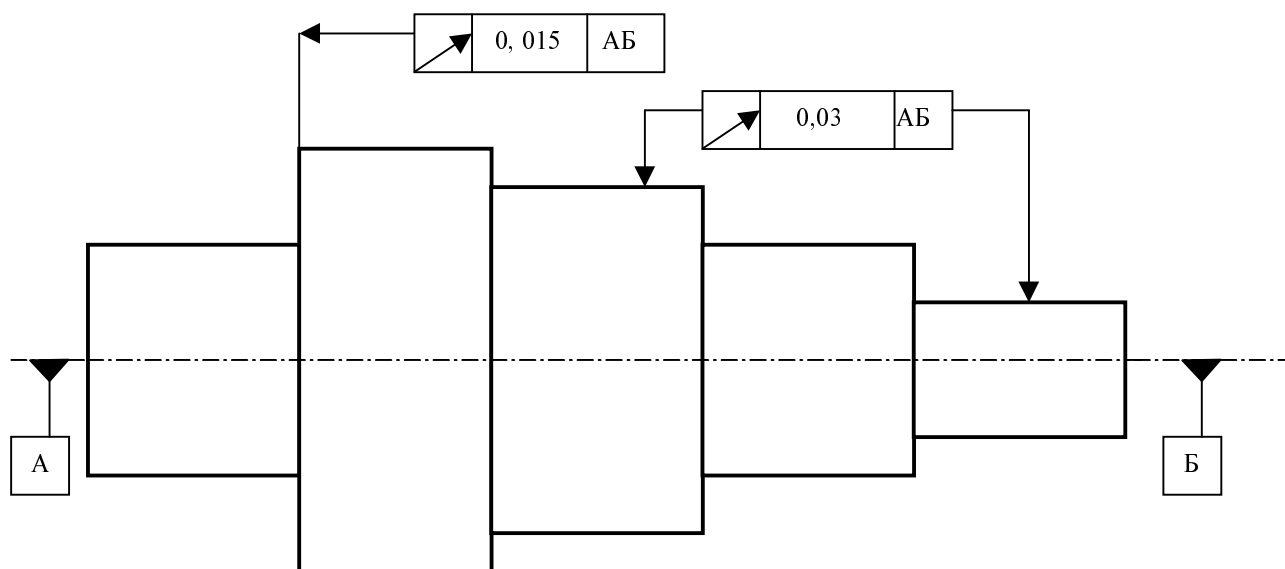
Схема поверхонь виробу, що контролюються
